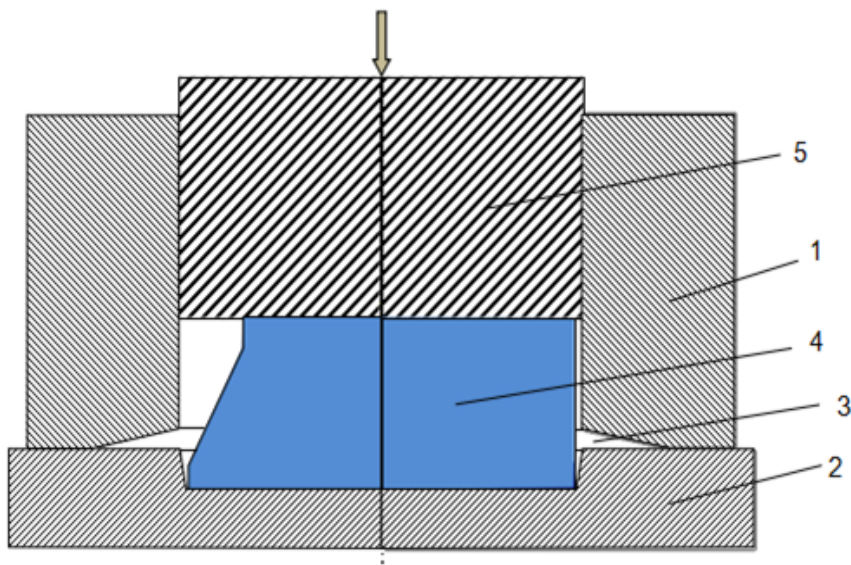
Розрахункова схема штампі з роз'ємними матрицями для штампування заготовок циліндричної форми (праворуч) та зрізаного конусу (ліворуч)
